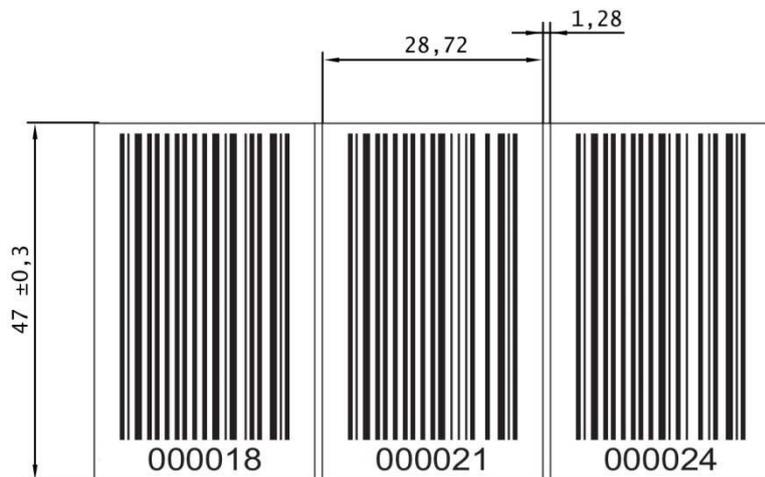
Maßzeichnung Barcodeband BCB G30 im 30 mm Raster (alle Maße in mm)
